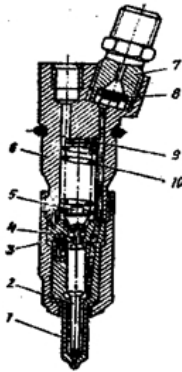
Форсунка: 1 - корпус распылителя; 2 - гайка распылителя; 3 - проставка; 4 -установочные штифты; 5 - штанга; 6 - корпус; 7 - уплотнительное кольцо; 8 - штуцер; 9 - фильтр; 10 -уплотнительная втулка; 11,12 - регулировочные шайбы; 13 - пружина; 14 - игла распылителя.
